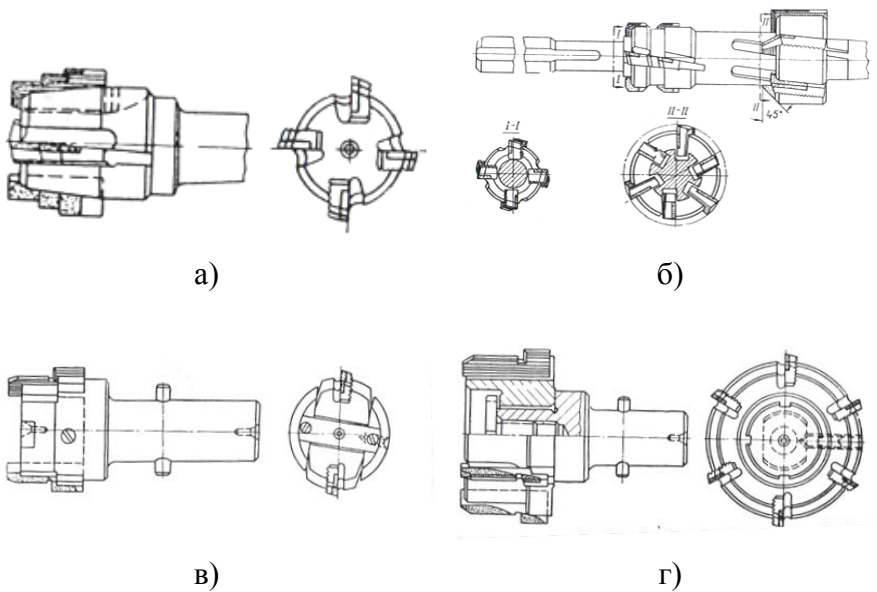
КОІ зі вставними ножами: а – зенкер зі ступінчастими ножами; б – чотириступінчастий зенкер; в – розвертка з ножами, оснащеними плаваючими пластинами; г – розвертка з плаваючим корпусом
